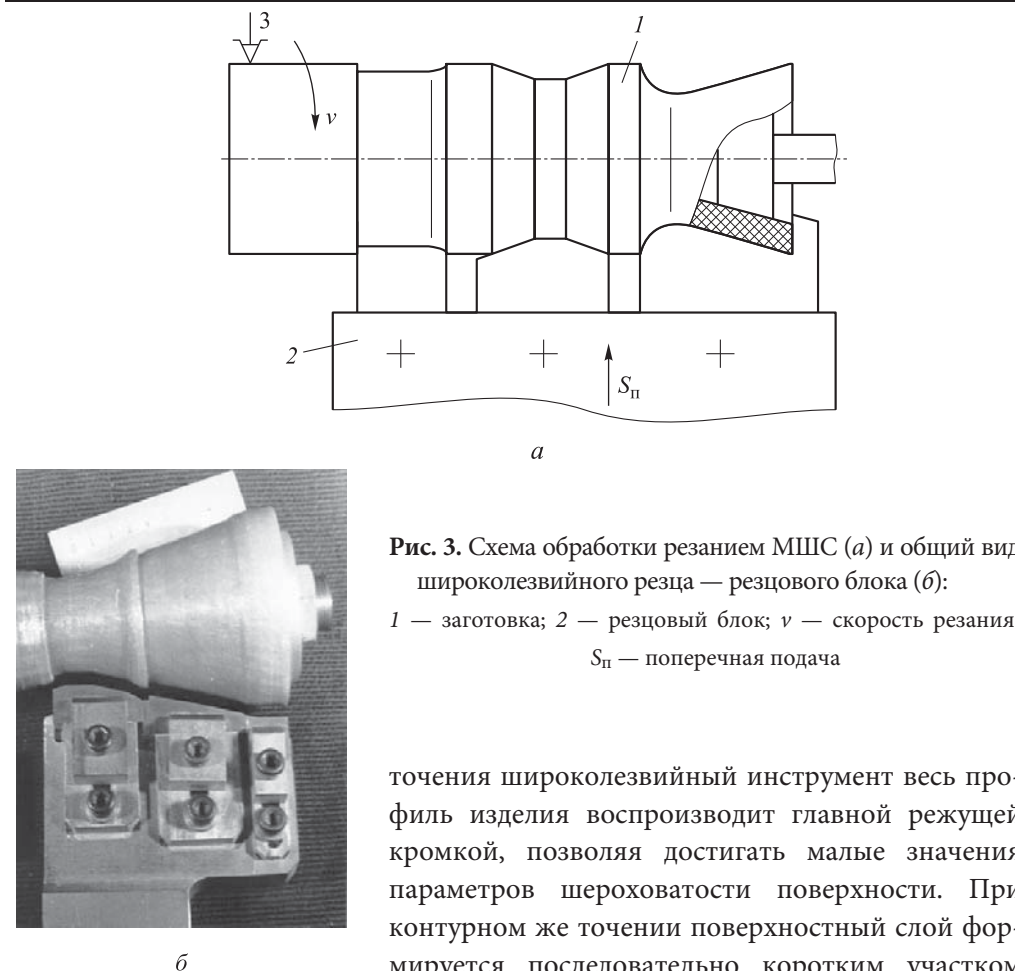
Схема обработки резанием МШС (а) и общий вид широколезвийного резца — резцового блока (б):
